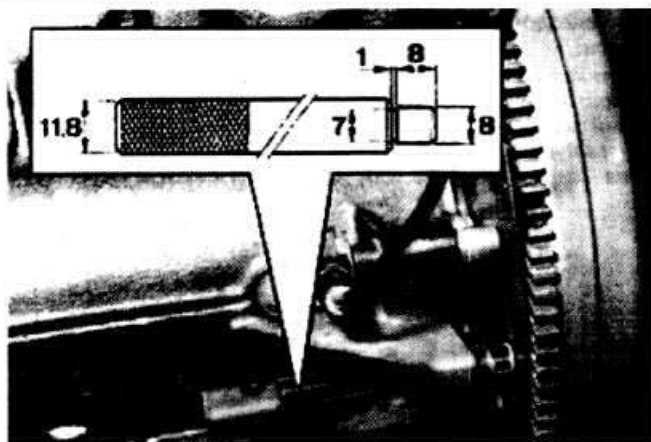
Блокировка фиксатором коленчатого вала в положении, соответствующем ВМТ поршня 1-го цилиндра
